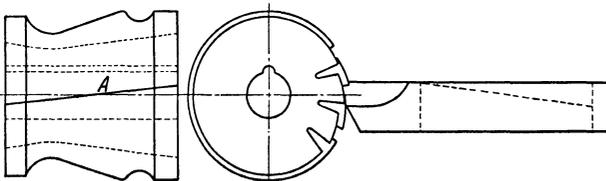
Hinterdrehen eines Fräasers mit Spiralzähnen.
